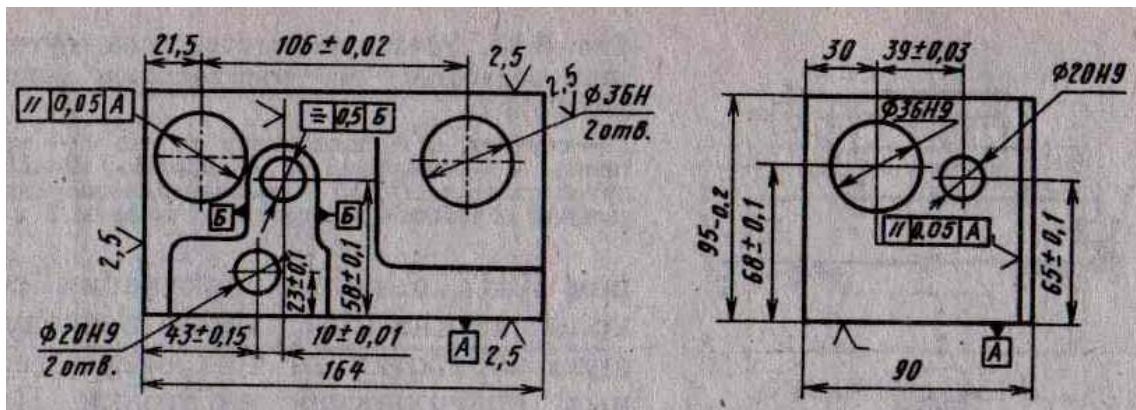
Эскиз корпусной детали, изготавливаемой на многоцелевом станке
